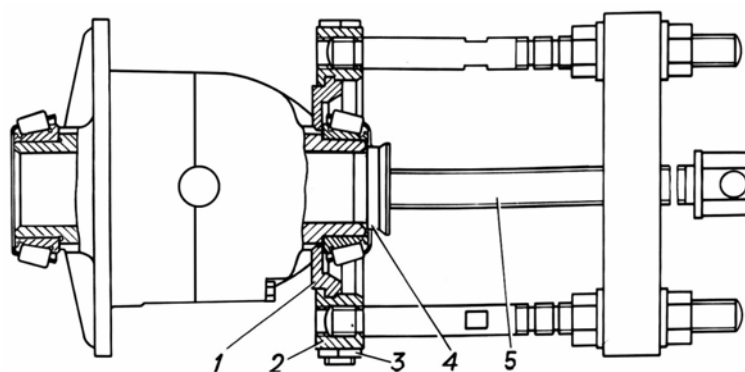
Снятие внутреннего кольца подшипника с коробки дифференциала: 1 – вкладыш; 2 – опора; 3 – гайка; 4 – подпятник; 5 – винт съемника
